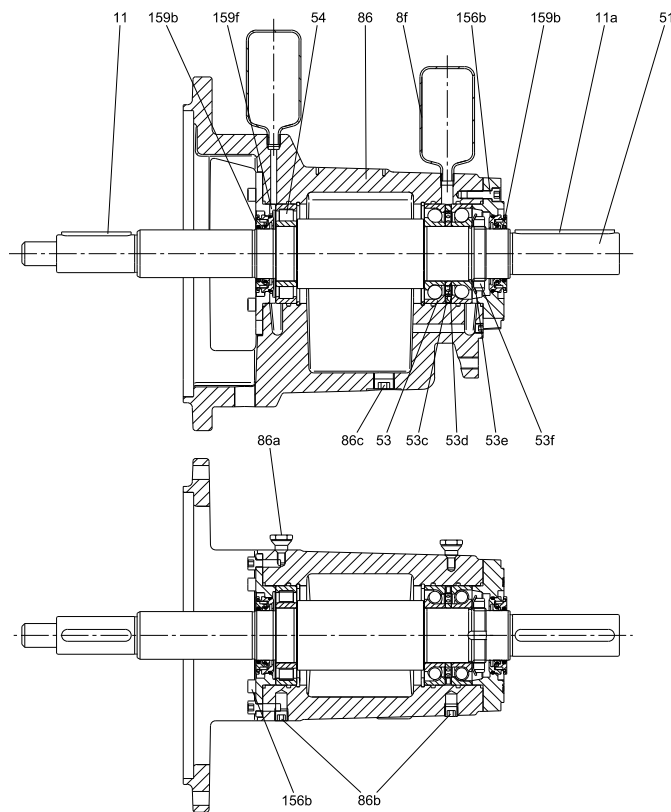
Подшипниковый узел NKG с консистентной смазкой
